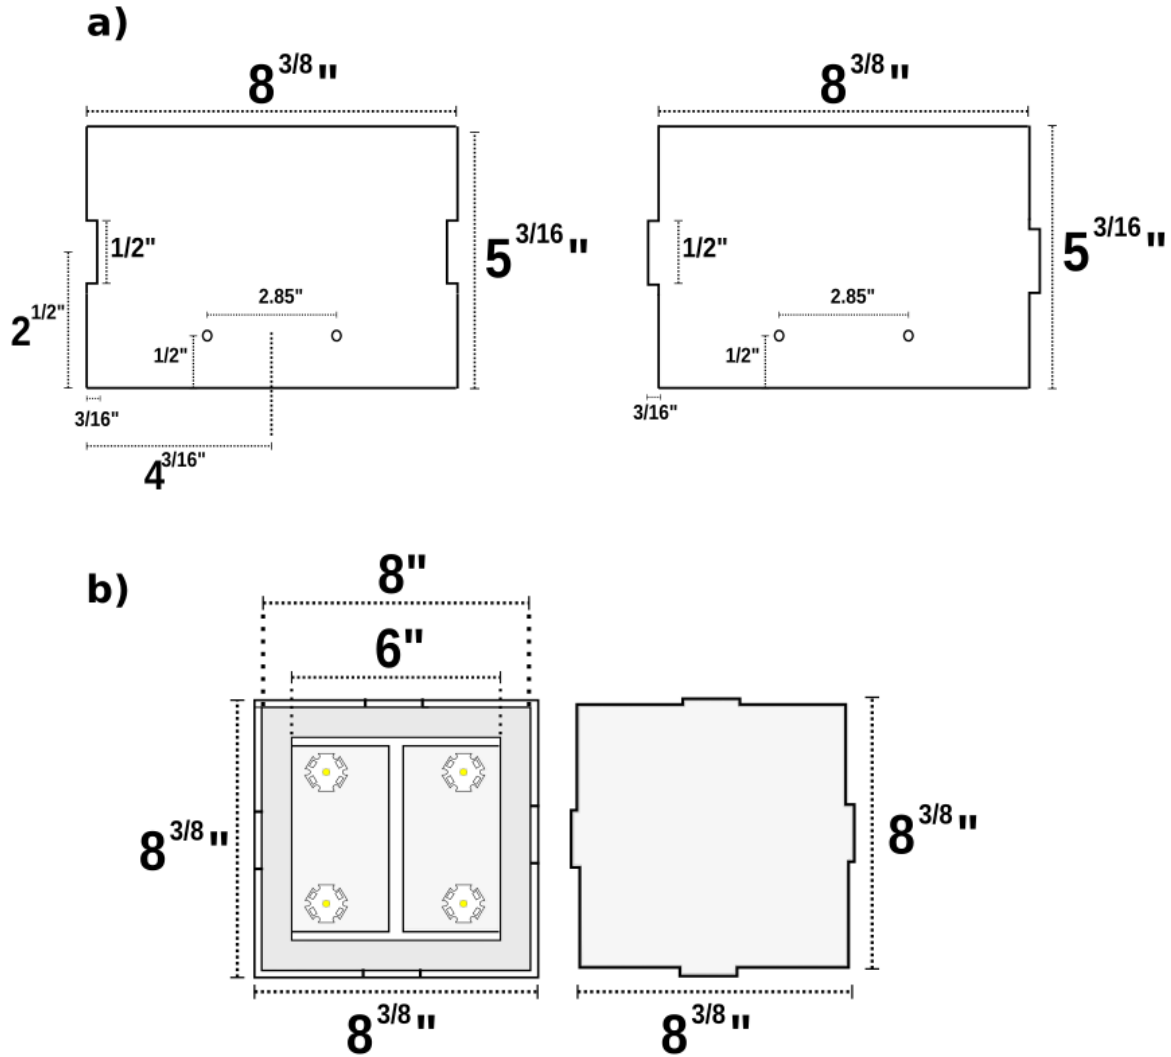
Esquema 2D del diseño propuesto para el montaje de HB LEDs. a) Dimensiones de las paredes del sistema, y b) Dimensiones del sistema ensamblado y panel difusor (vista superior).
